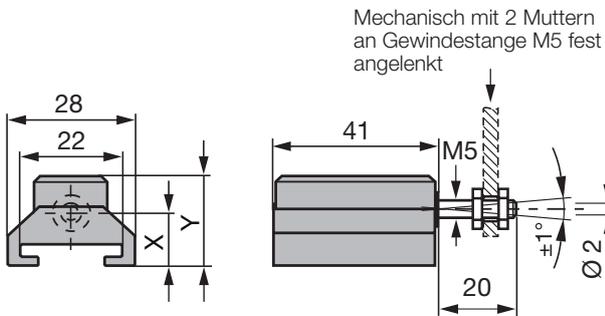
Einbaumaße Positionsgeber BTL5-M/N-2814-1S
